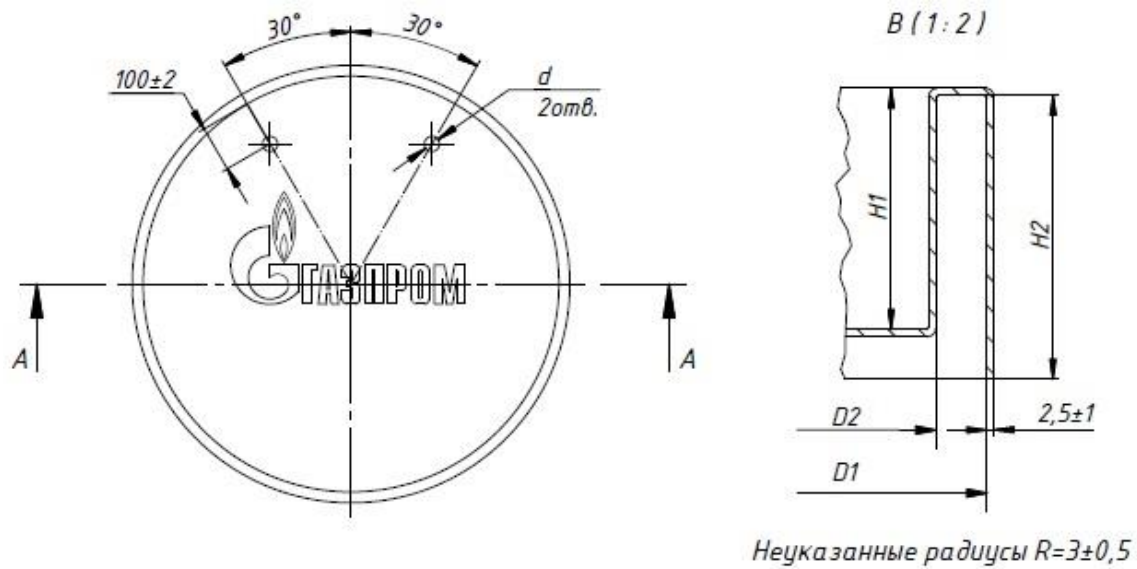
Стандартная конструкция и размеры полимерных заглушек
